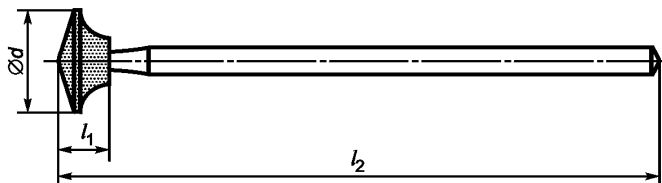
С режущей кромкой (конус, обратный гиперболоидальный) головка
